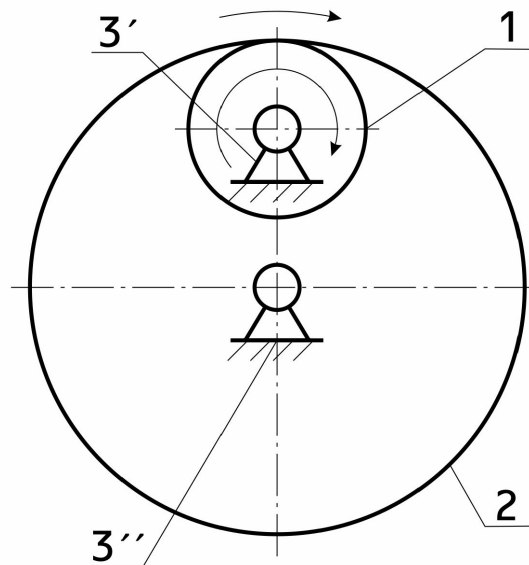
Зубчатый механизм с внутренним зацеплением
